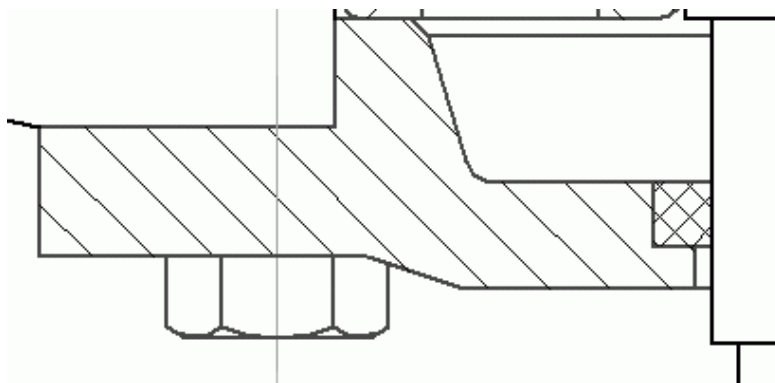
Фиксирующий винт сквозной крышки ведущего вала
